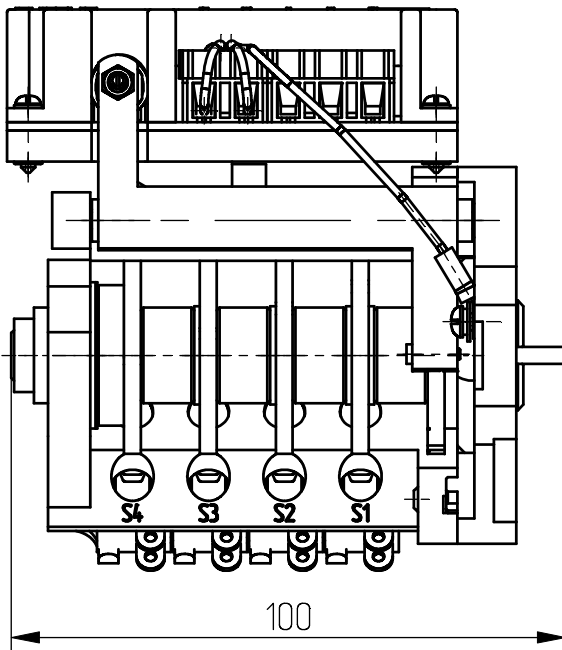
Общий вид, габаритные и установочные размеры блока БД-10АМ-0
